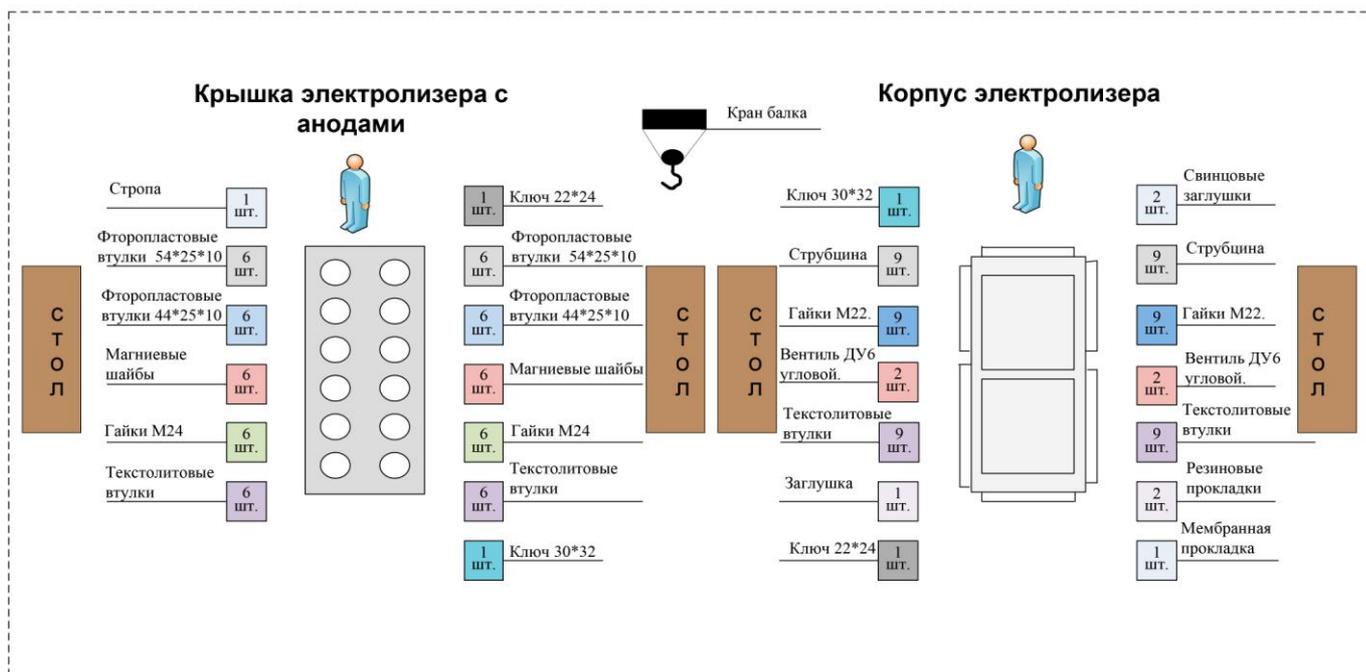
Стандарт необходимого инструментария и запчастей для сборки
